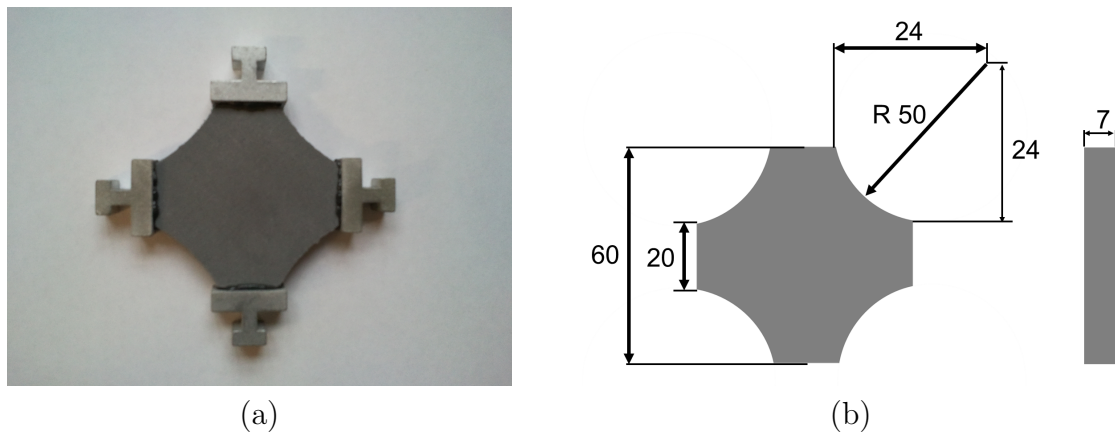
(a) Éprouvette en croix utilisée pour les essais bi-axiaux avec les mors collés à chaque extrémité permettant de la fixer à la machine. (b) Dimensions et géométrie de l'éprouvette retenue, forme en croix avec un très grand rayon du congé de raccordement.
